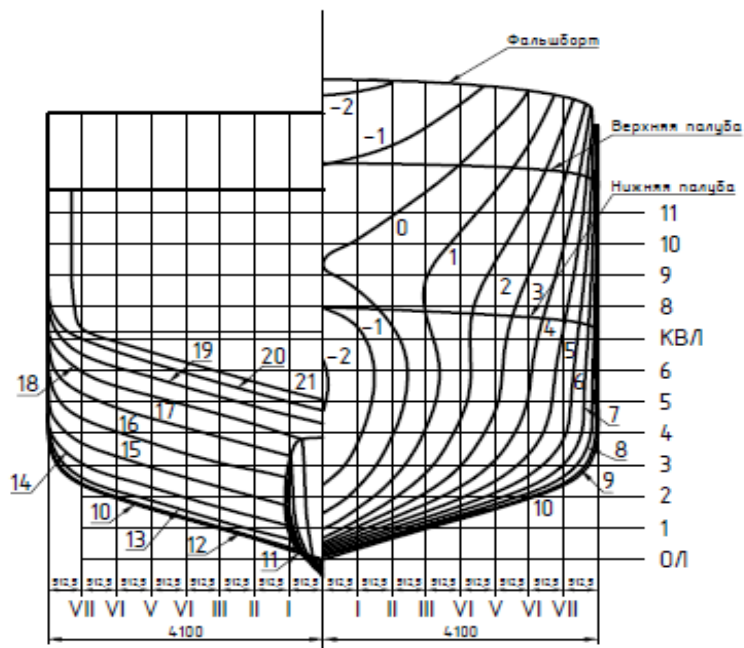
Теоретический корпус с бульбовыми обводами по норвежскому типу
